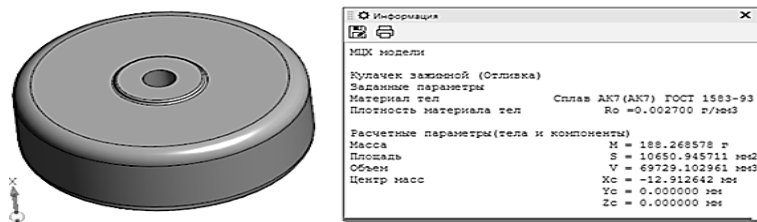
Расчёт массы заготовки, полученной способом литья под давлением
